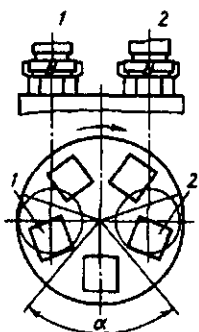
Схема многоместной параллельно-последовательной обработки на двухшпиндельном вертикально-фрезерном станке с карусельным столом: α – зона загрузки; 1 и 2 – фрезы
